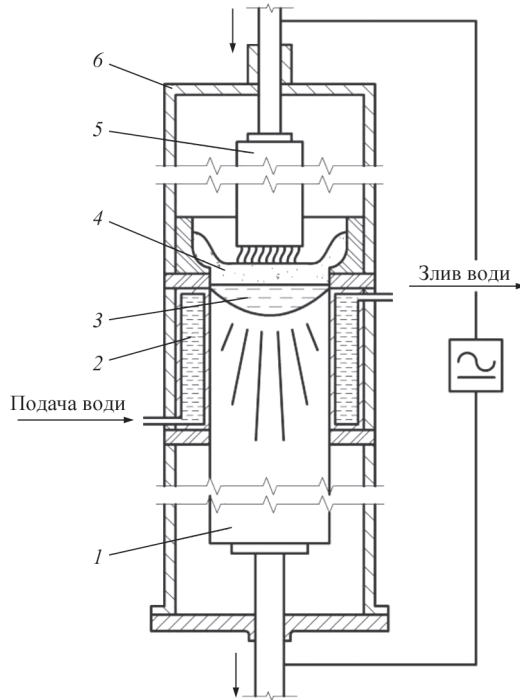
Схема дугошлакової печі з витратним електродом: 1 — зливка; 2 — кристалізатор; 3 — розплав; 4 — шлакова ванна; 5 — витратний електрод; 6 — плавильна камера
